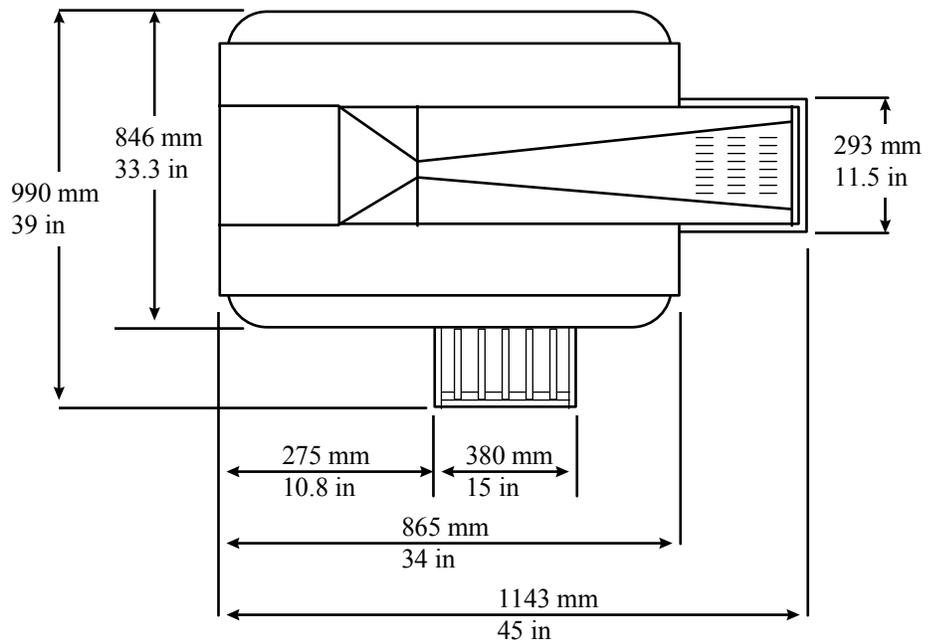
Dimensions SOLO™ Plus (Vue de dessus)
